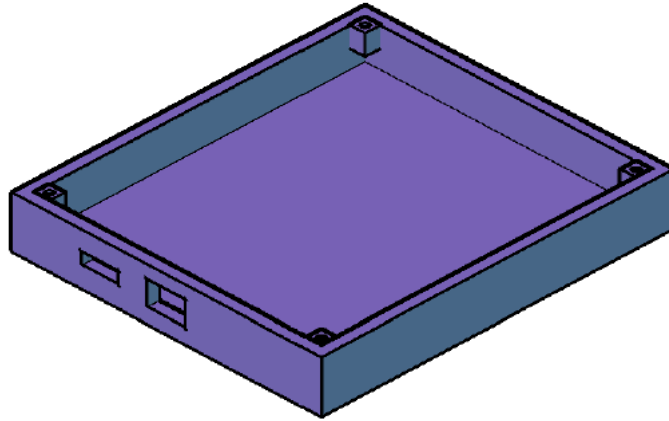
Diseño de la parte inferior del prototipo en AutoCAD 3D.
